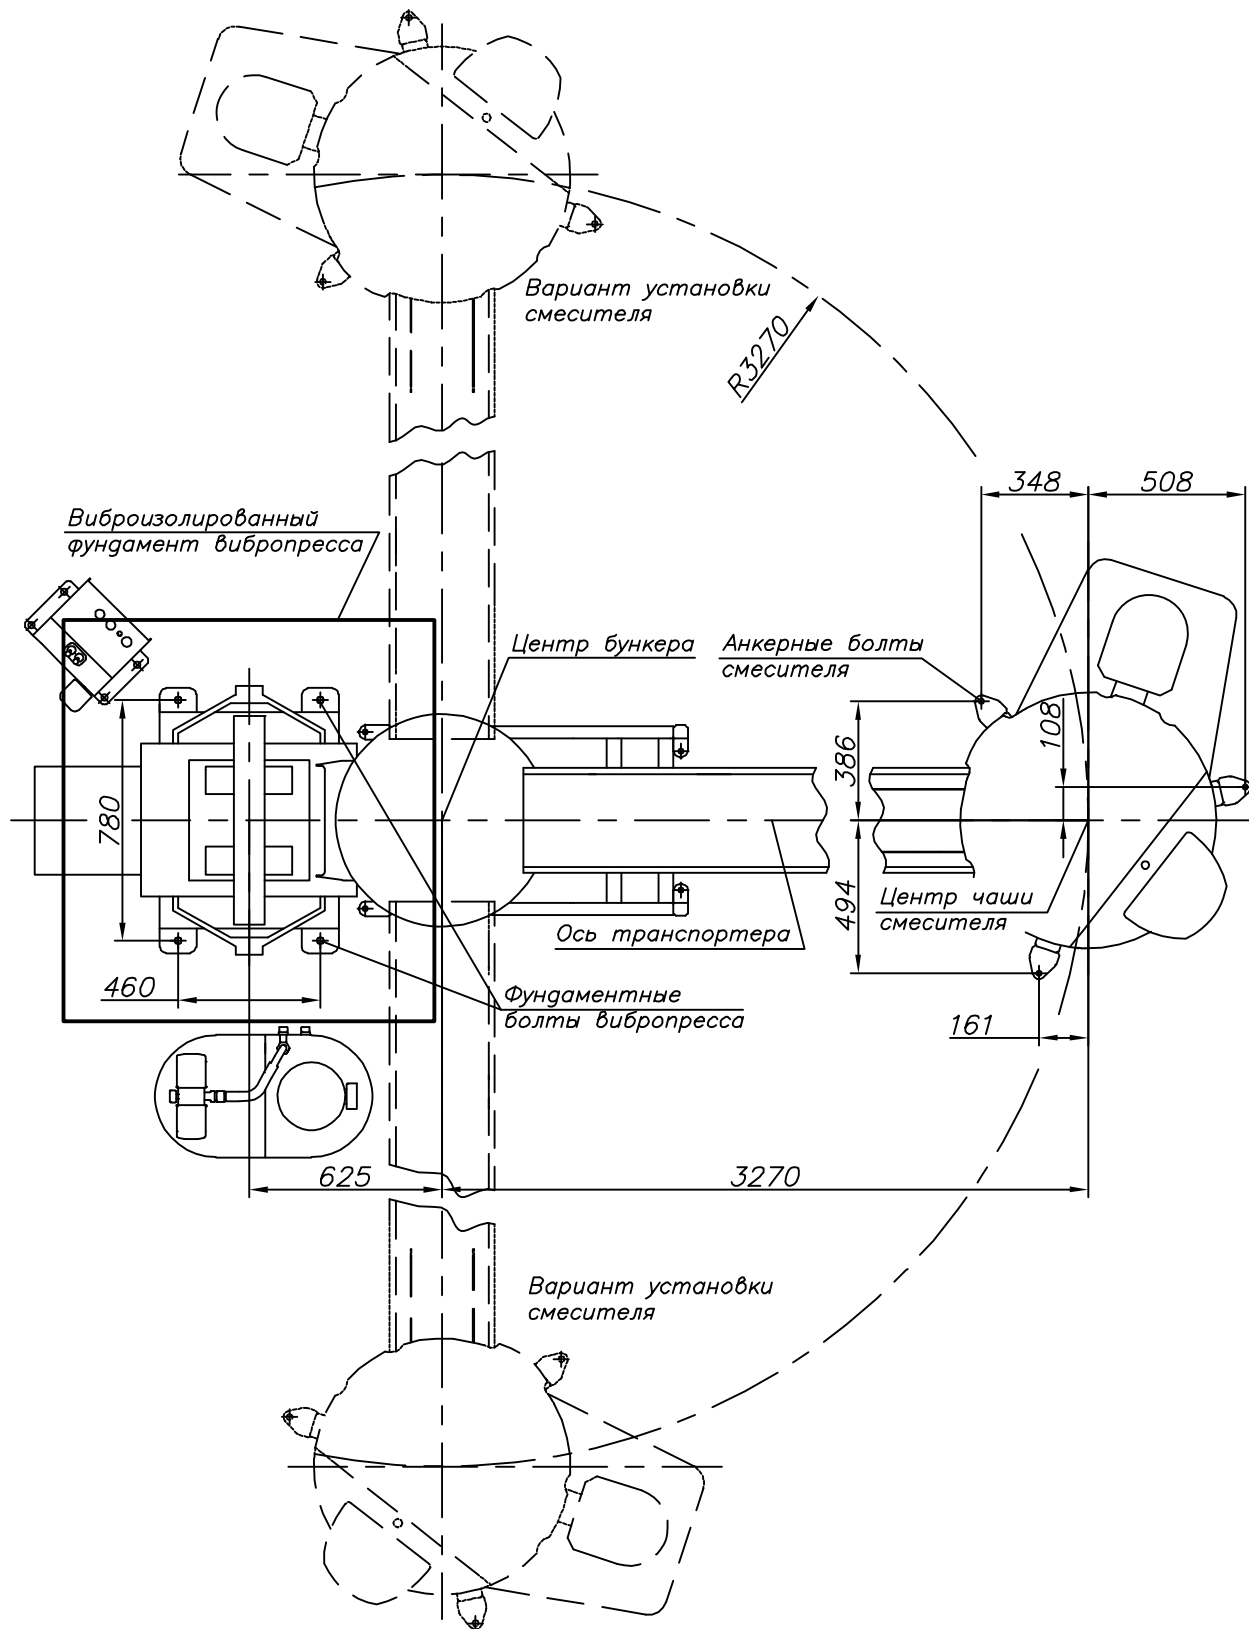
Схема установки вибропрессов, бункера и смесителя.
